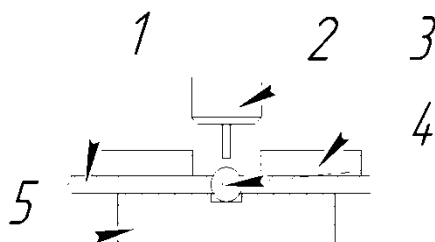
Пример применения сухого льда: 1 – свариваемые детали; 2 – сварочная головка; 3 – сухой лёд; 4 – сварочный шов; 5 – подкладка
